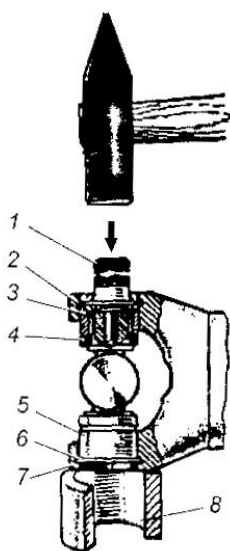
Разборка карданного вала: 1 — оправка; 2 — игольчатый подшипник; 3 — крестовина; 4 — уплотнительная манжета; 5 — стакан; 6 — ступица; 7 — пыльник; 8 — кольцо
